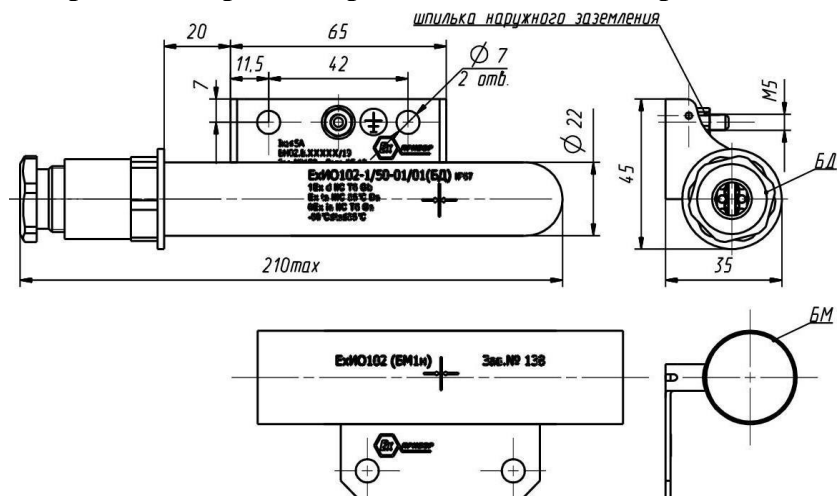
Габаритный чертёж извещателя ЕхИО102-1/50
